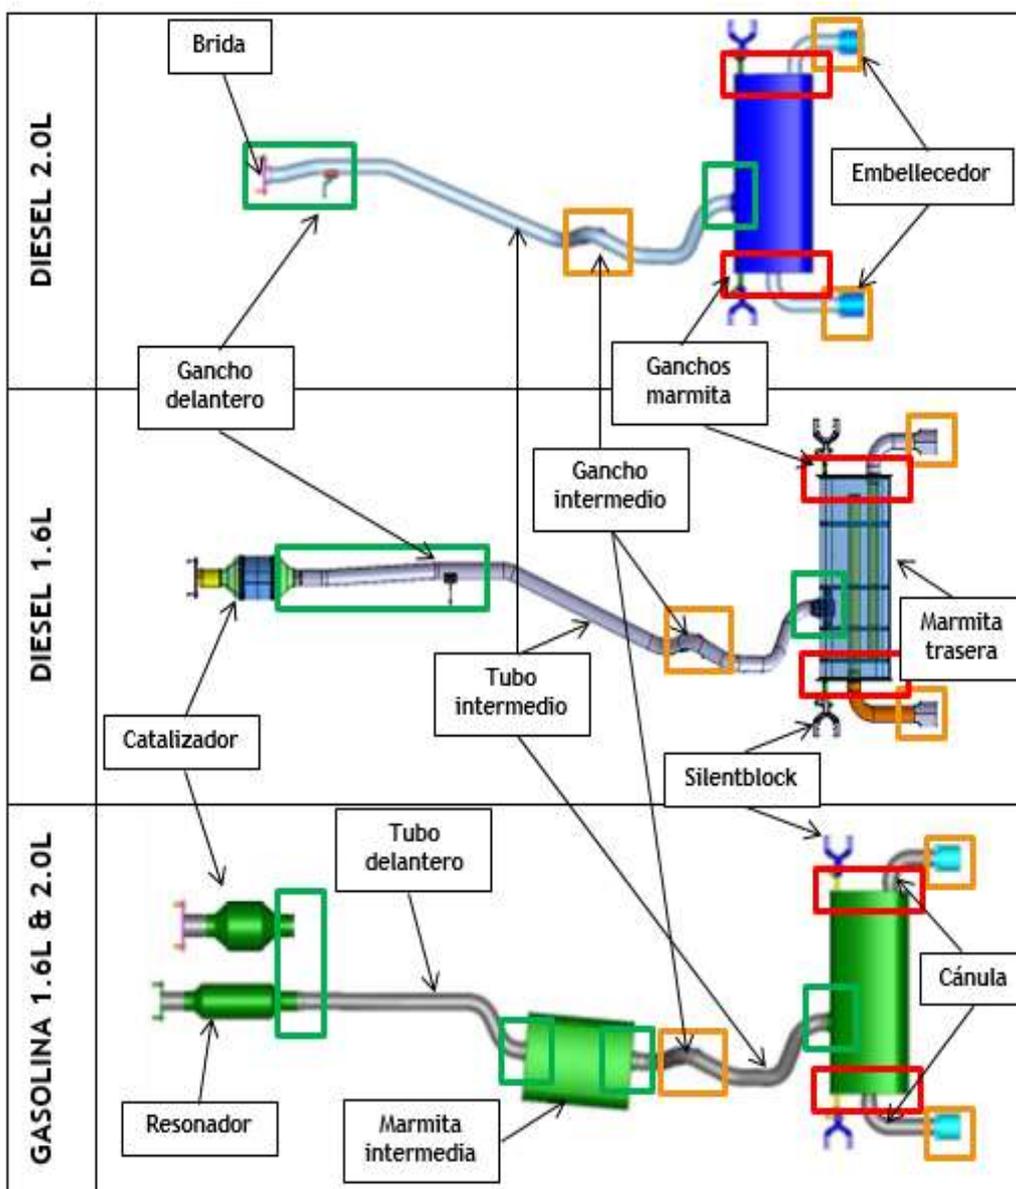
Componentes de cada tubo de escape y robots para cada soldadura. (Producción propia)
